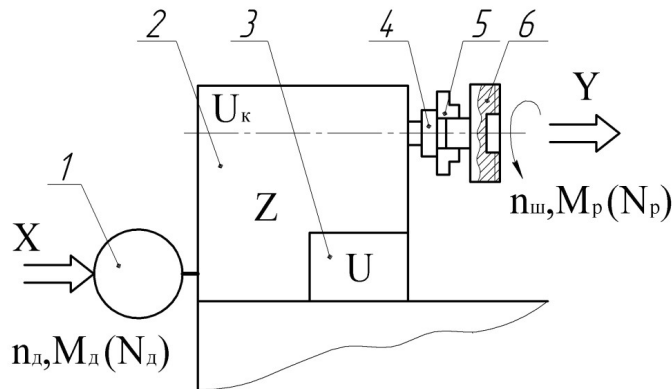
Привод головного руху токарного верстату з різними системами керування
